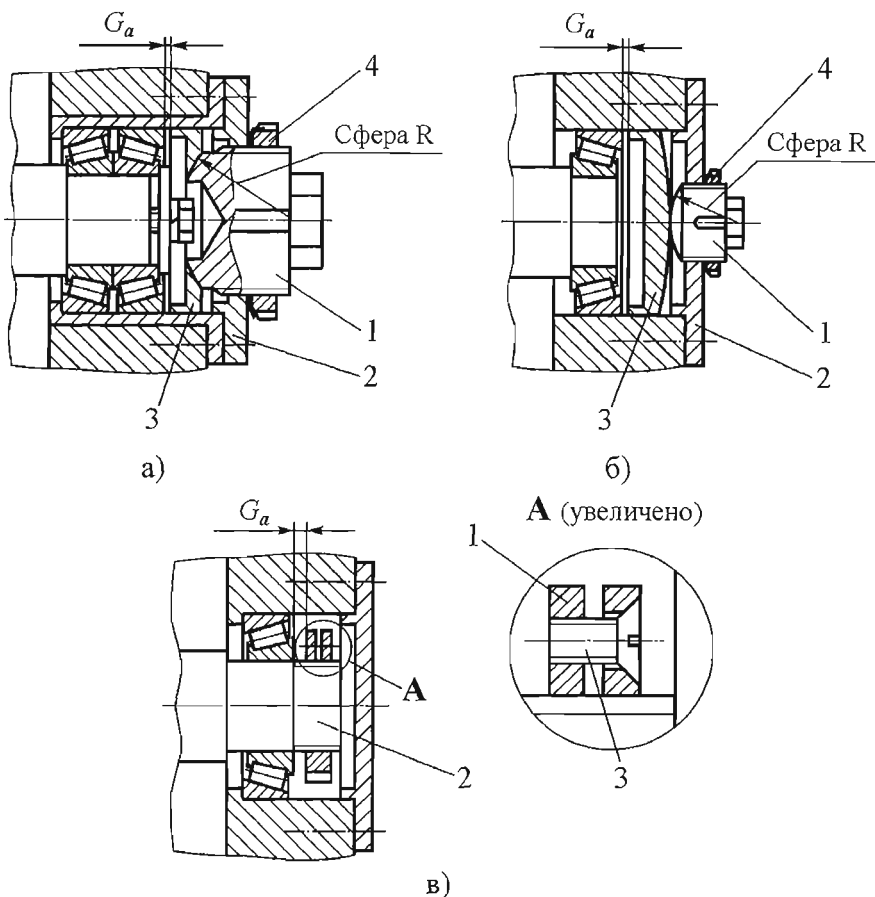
Конструкции подшипниковых узлов, регулируемых резьбовыми деталями:
